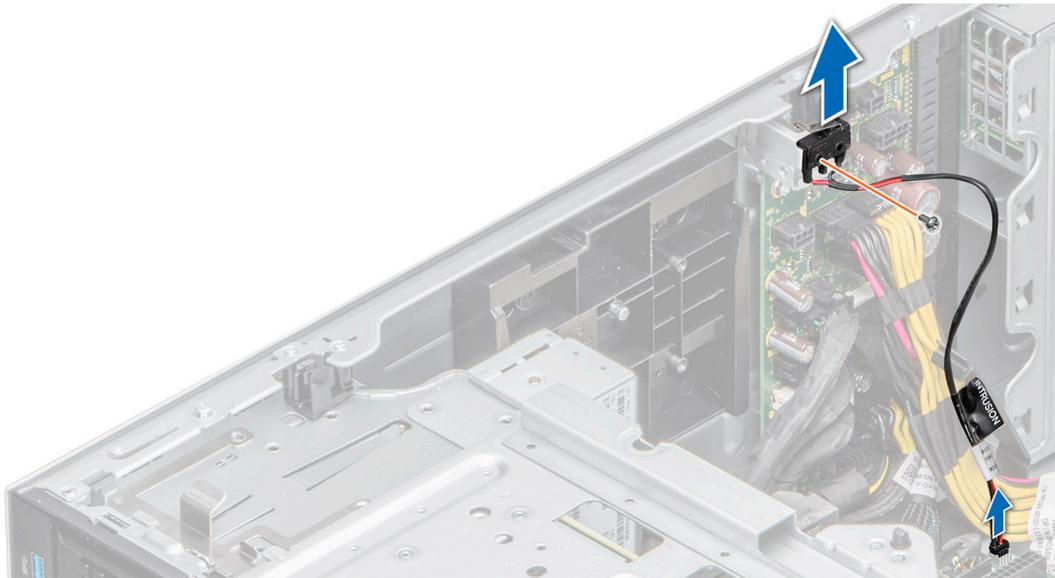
Entfernen des Eingriffsschaltermoduls
